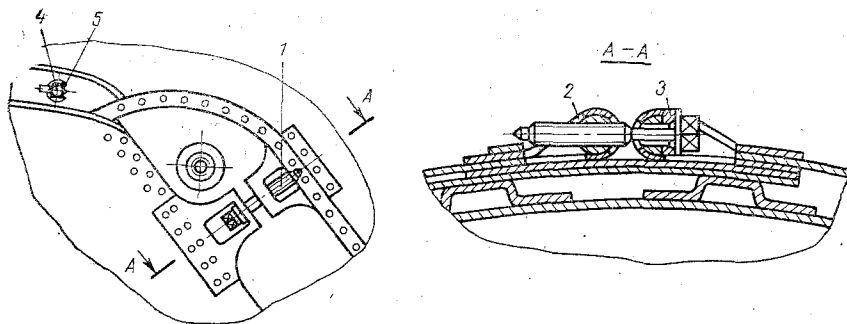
Эскиз выхлопного патрубка с измененной конструкцией крепления половин кожуха:
